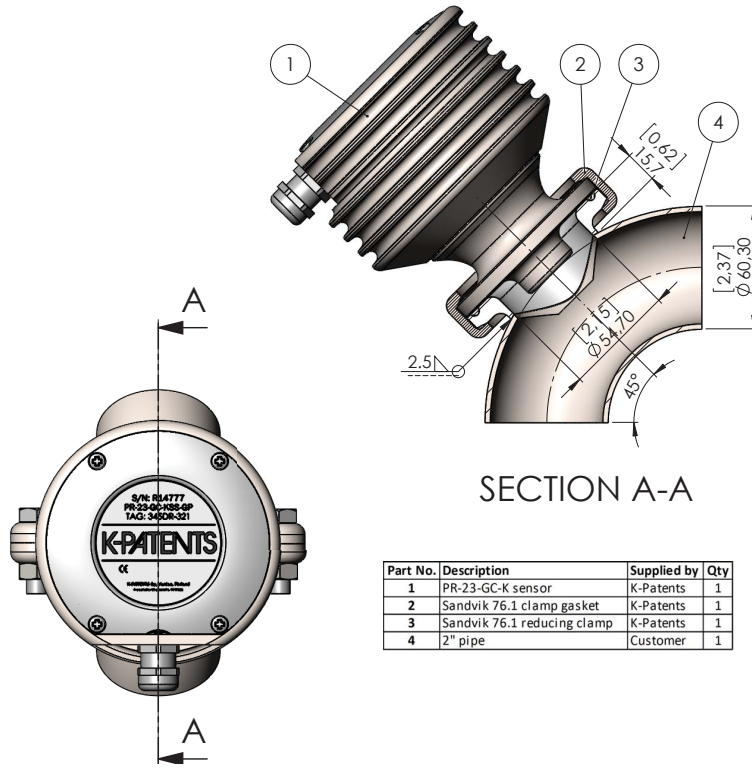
Installation du capteur dans un tube de 2 pouces
